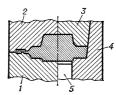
Условная схема штампа для объёмной штамповки: 1 — нижняя по-ловина; 2 — верхняя половина; 3 — пуансон; 4 — матрица; 5 — выталкиватель.
